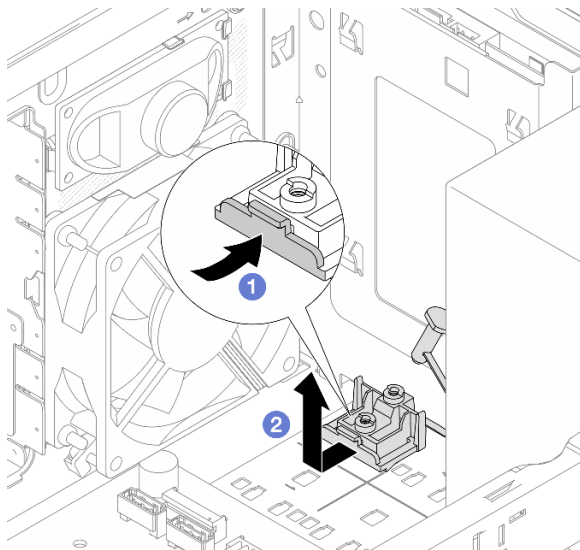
Entfernen der M.2-Laufwerkhalterung
